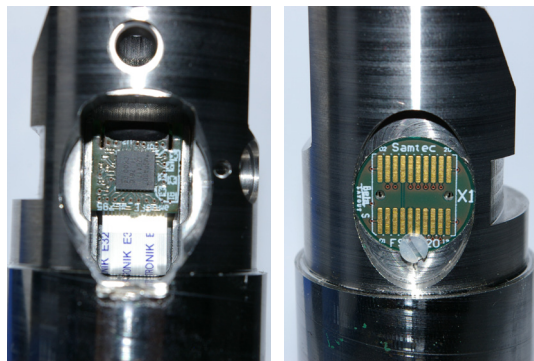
Bildausschnitt - Versuchswerkzeug mit integriertem Messsystem
